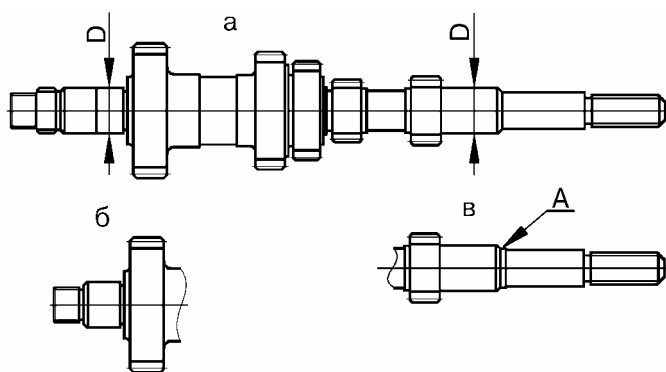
Вал первичный: а – 2110-1701030; б – 2108-1701030; в – 21083-1701030.
